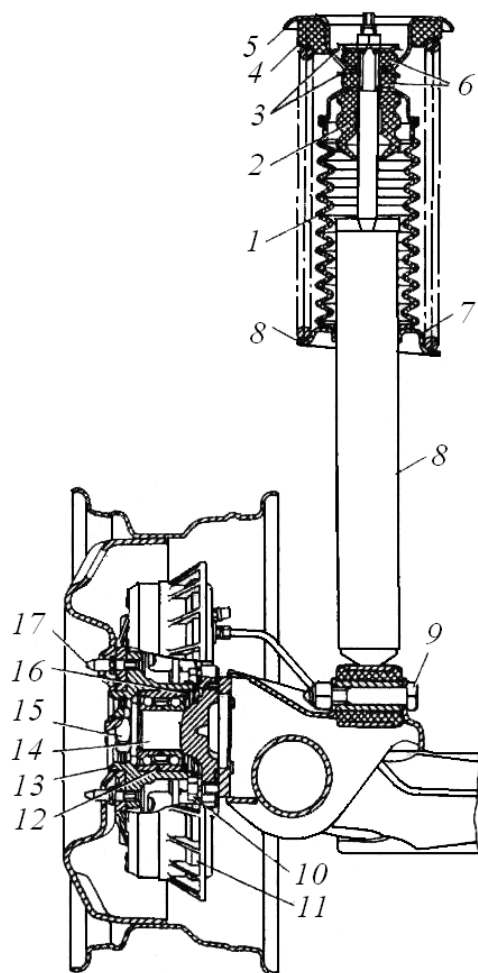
Задний мост с амортизатором ВАЗ 2108: 1 – защитный кожух; 2 – буфер хода сжатия; 3 – опорная шайба; 4 – изолирующая прокладка пружины; 5 – верхняя опорная чашка пружины подвески; 6 – подушки крепления штока амортизатора; 7 – нижняя опорная чашка пружины; 8 – амортизатор; 9 – болт крепления амортизатора; 10 – болт крепления оси ступицы колеса; 11 – тормозной барабан; 12 – подшипник ступицы; 13 – ступица колеса; 14 – ось; 15 – гайка; 16 – стопорное кольцо; 17 – установочный штифт
